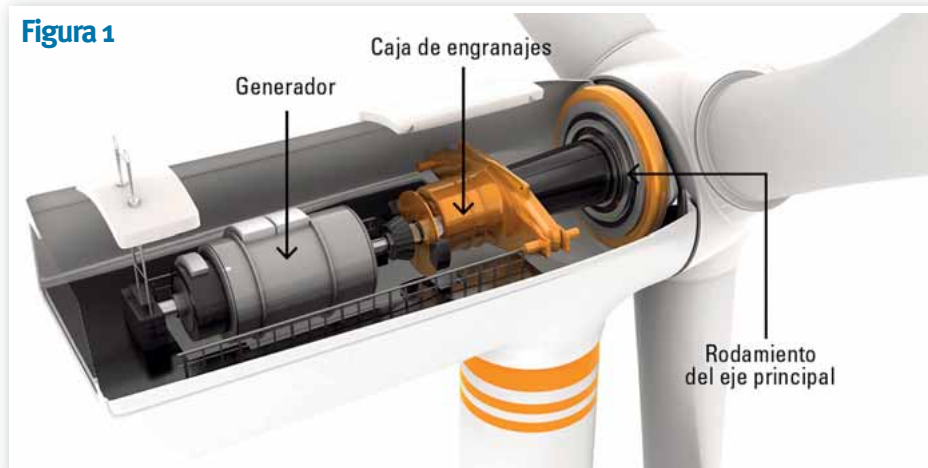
El diseño de SRB de montaje de tres puntos se soporta en el rodamiento del eje principal y dos brazos de torsión reactivos en la caja de engranajes.
